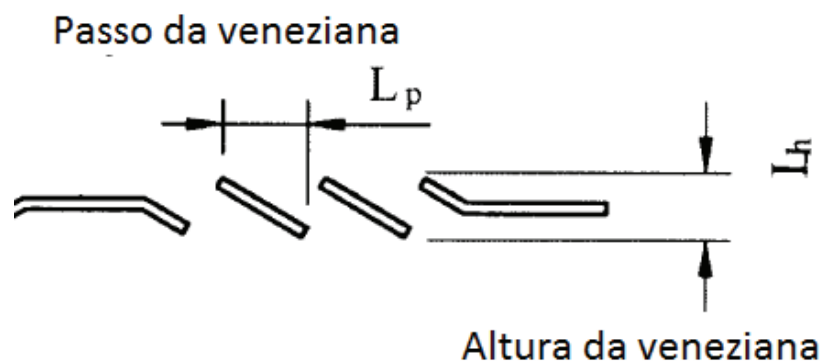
Vista em corte da aleta plana com venezianas.
